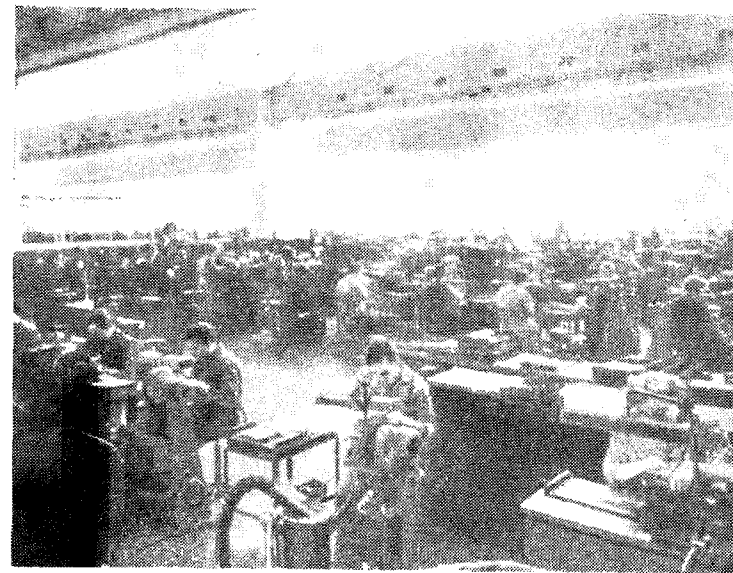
Общий вид крупного цеха обработки твердосплавных пластинок (Ф. Крупп, завод «Видна»)
